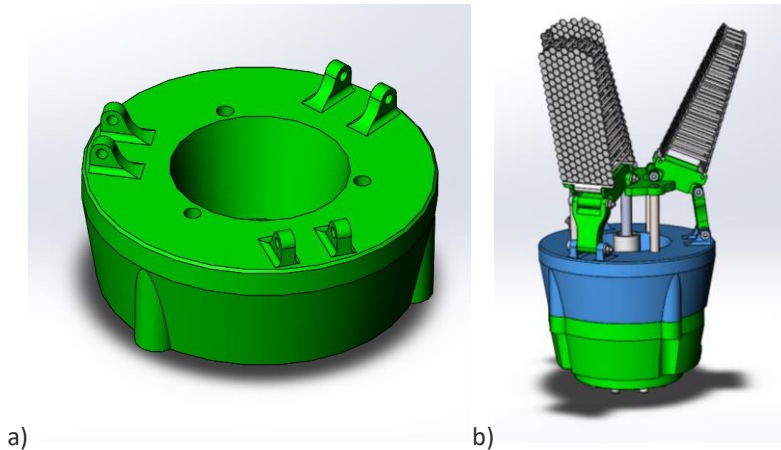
Base superior - vista do componente (a) e montagem no conjunto (b).
